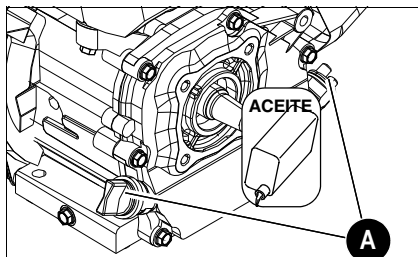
Rellenar aceite de motor (motor de gasolina)
